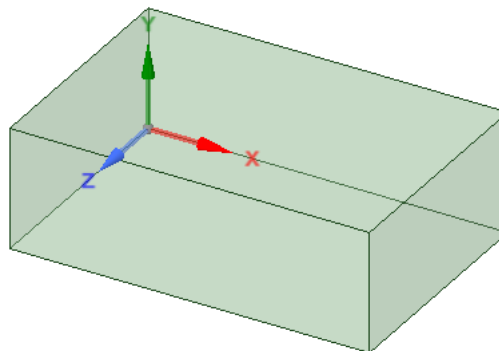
C Posizionamento Sul piano XZ con base sul piano YZ.
